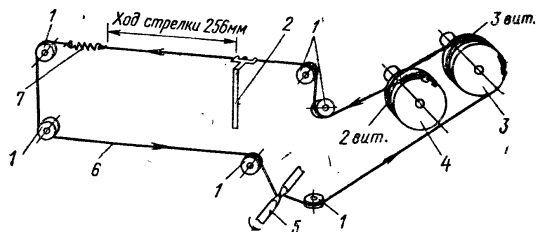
Кинематическая схема верньерного устройства «Вега-312»
